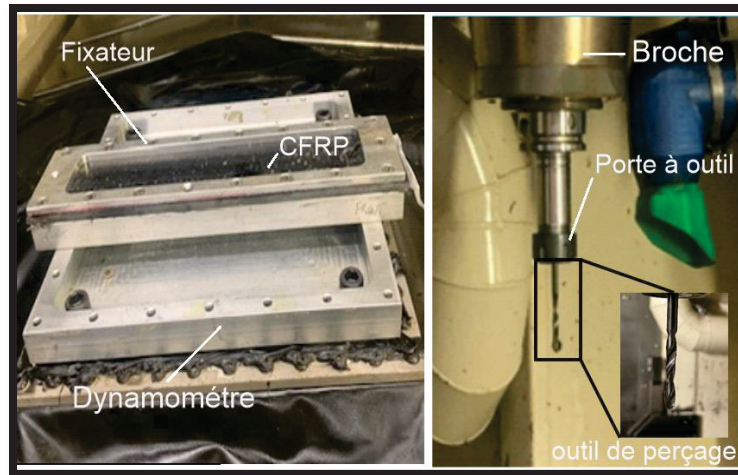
Montage de l'outil de coupe et du dispositif d'usinage sur la table dynamométrique
